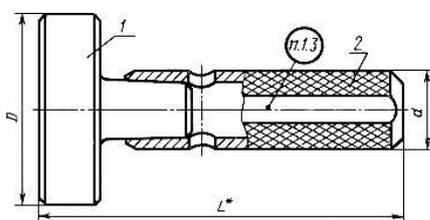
Конструкция и размеры гладких калибров-пробок со вставками НЕ
